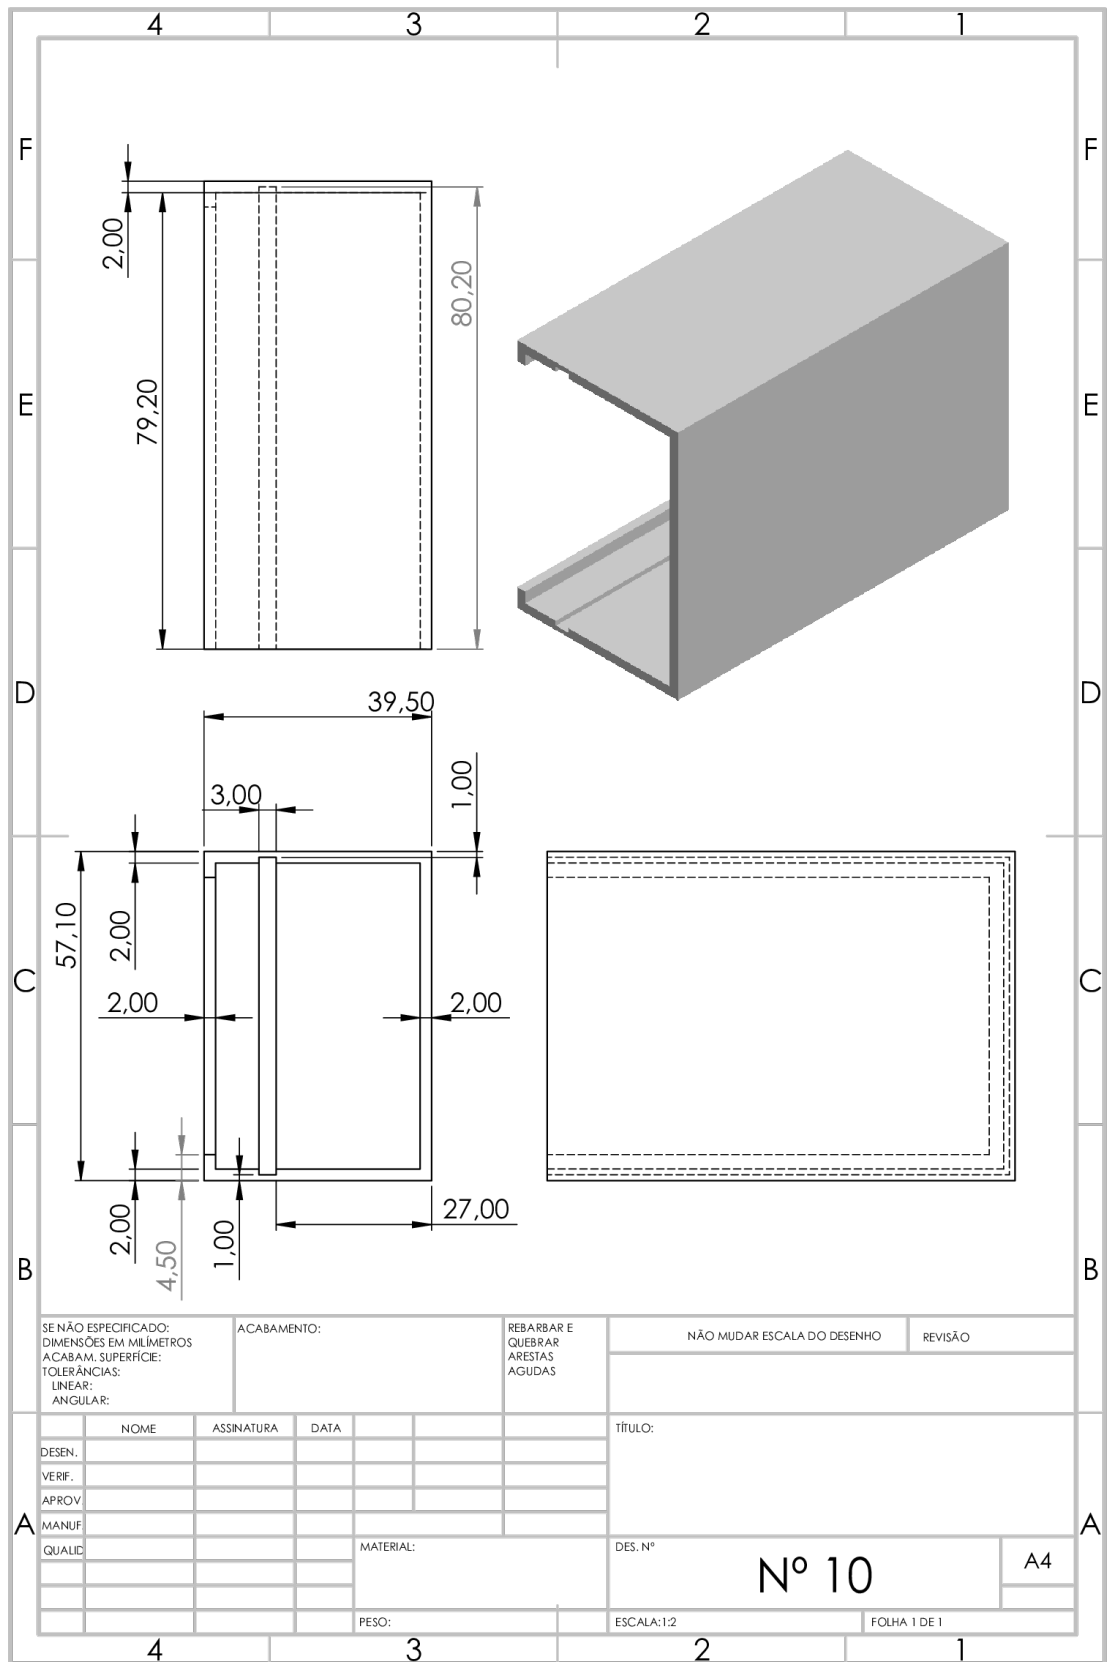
Desenho Técnico da Capa e Suporte de Difusor para Placa de LEDs das Laterais
